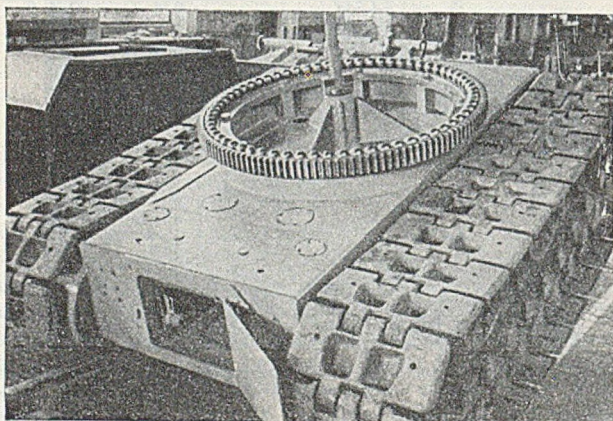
Raupenunterwagen des Universalbagger B 323 mit aufgesetztem Zahnkranz, Rollenring und hohler Mittelwelle.
